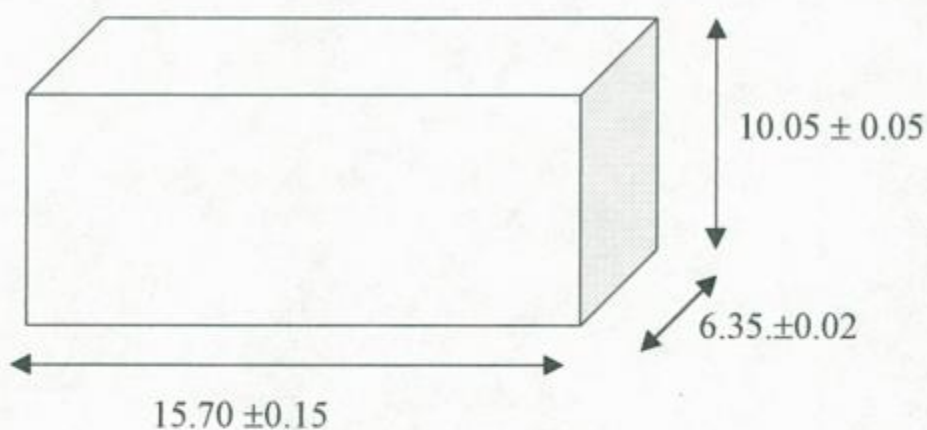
Dimensiones y forma geométrica de la probeta.
